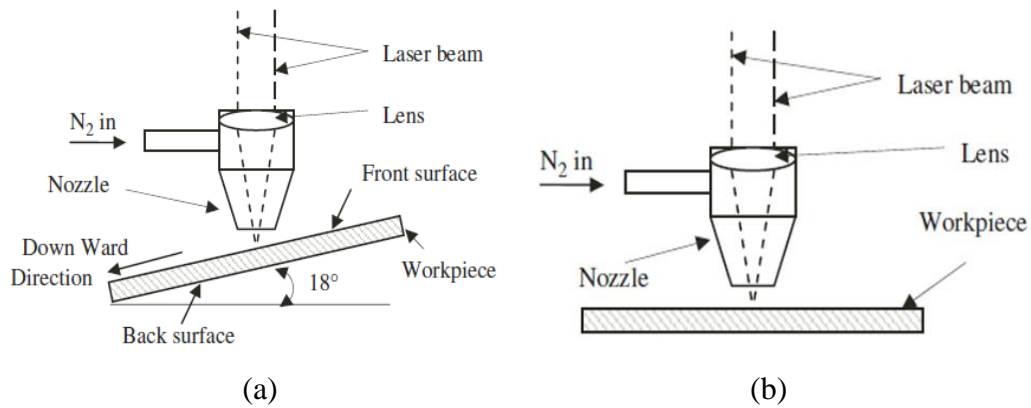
(a) Corte inclinado, (b) Corte tradicional
